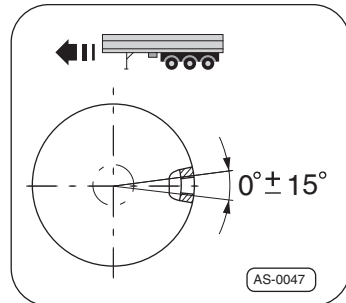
· Préparer le tube d'essieu avec l'alésage pour le coude d'assemblage
